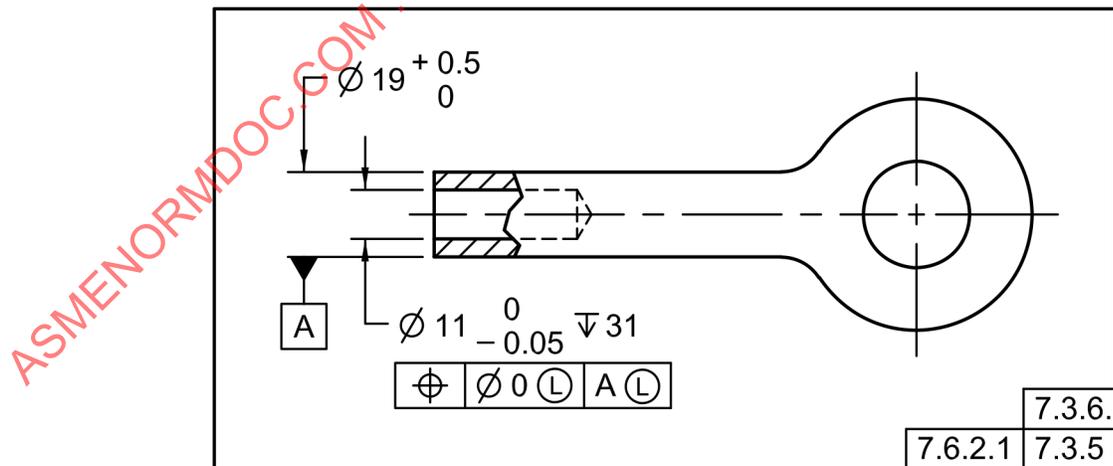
Elemento Datum Referenciado a MMB
